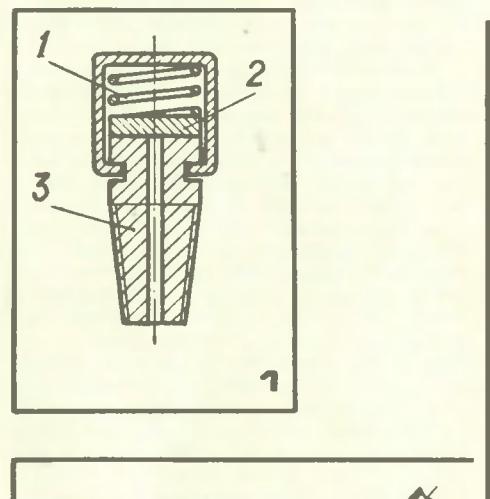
Пробка сапуна старой конструкции: 1 — пружина; 2 — диск; 3 — корпус.
